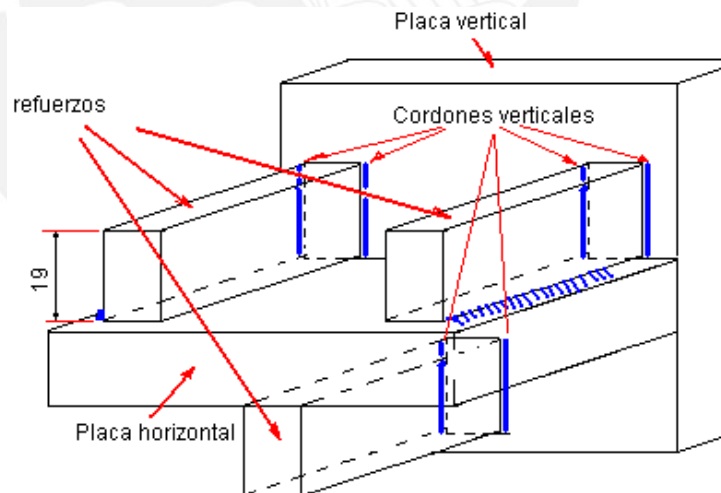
Esquema de cordones de soldadura entre placas de la torre fija 2.
